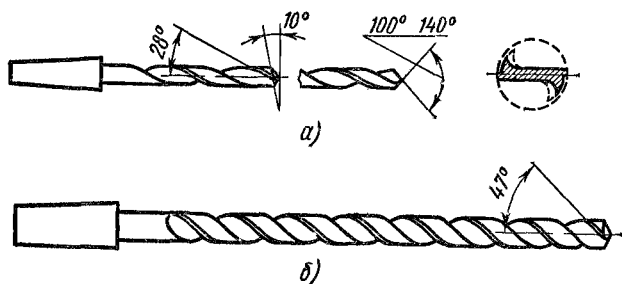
Сверло для сверления отверстий в магниевых сплавах
